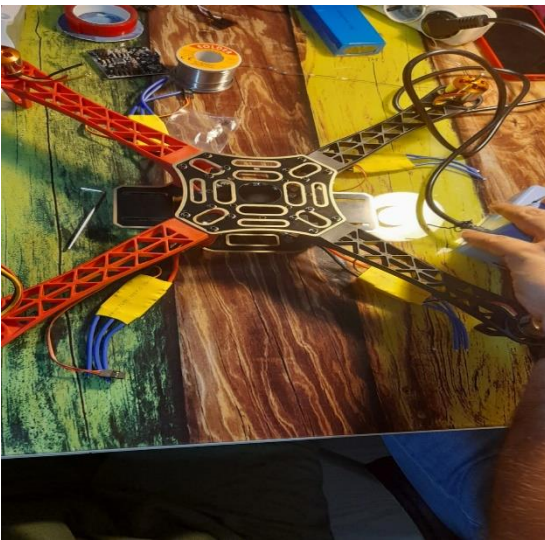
Gövde Parçalarının Montajı ve Prototipin Elde Edilmesi
